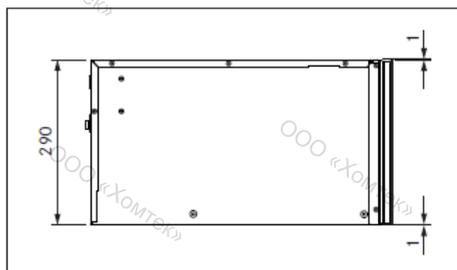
Размеры прибора, модель MSS290, вид сбоку
